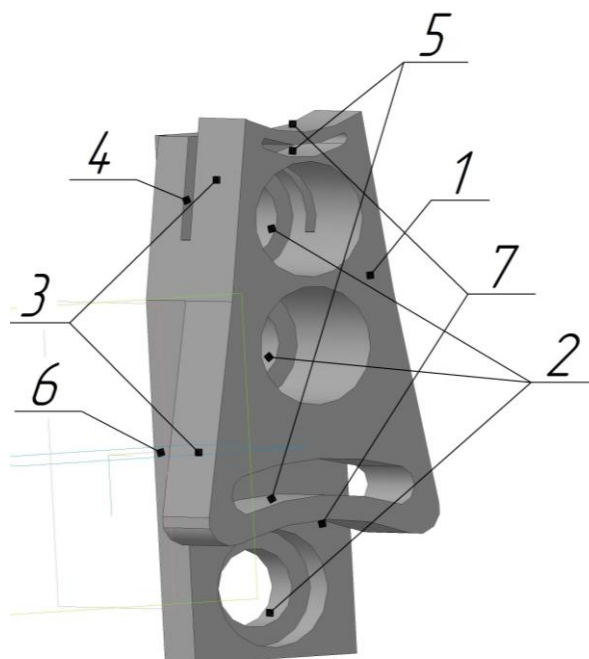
Конструкція адаптивного затискного кулачка для затиску двох різних діапазонів діаметрів оброблюваних заготовок.
